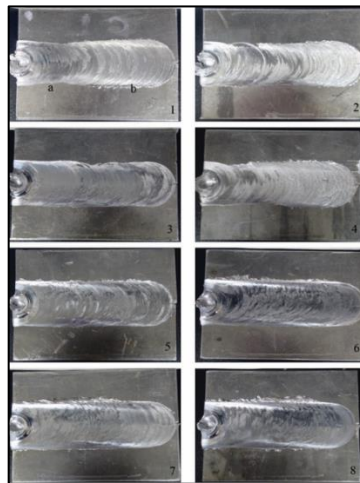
Piezas soldadas mediante FSW (Experimentación Inicial)
